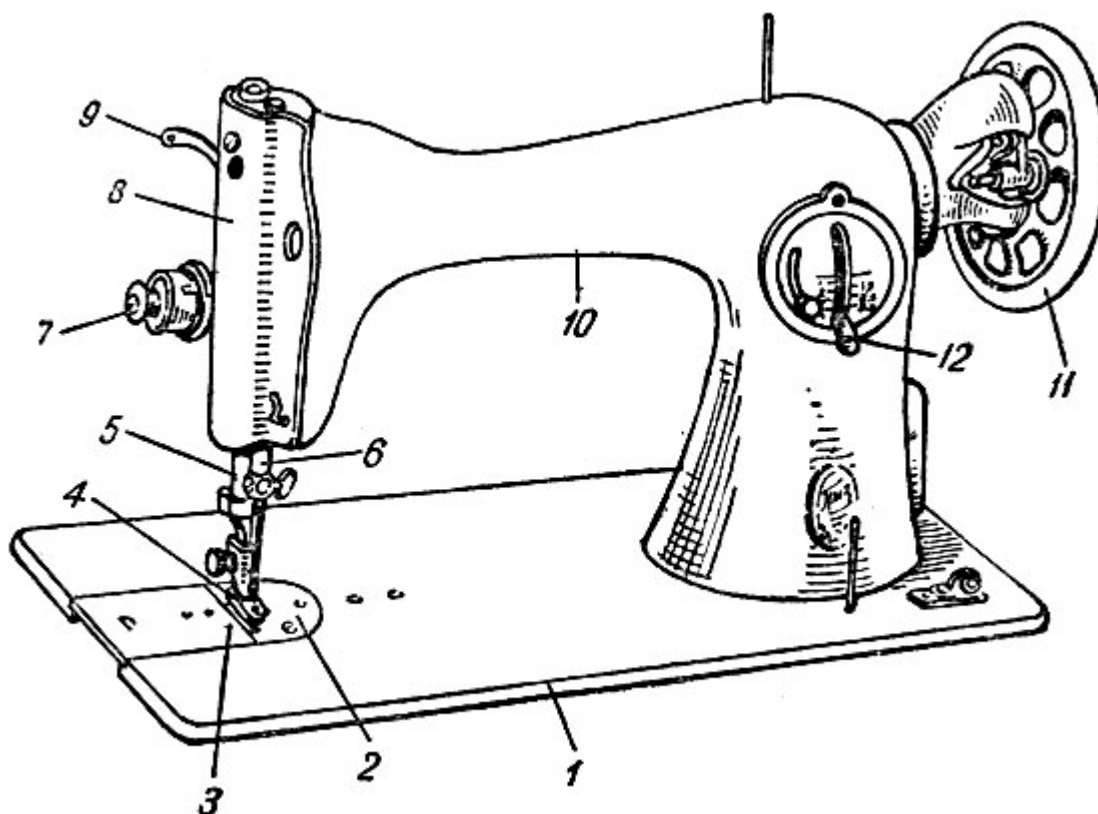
Основные части швейной машины: 1-А класса ПМЗ с центральношпульным челноком: 1 - платформа; 2 - игольная пластинка; 3 - задвижная пластинка; 4 - нажимная лапка; 5 - стержень нажимателя ткани; 6 - стержень игловодителя; 7 - гайка для регулирования натяжения верхней нитки; 8 - фронтальная доска; 9 - рычаг нитепритягателя; 10 - рукав; 11 - маховик; 12 - головочный винт регулятора строчки
